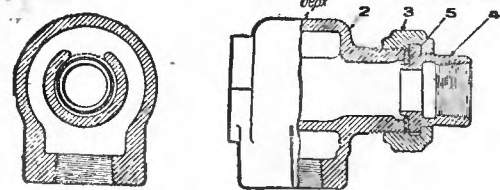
Предохранительный клапан локомотивного распределителя.
